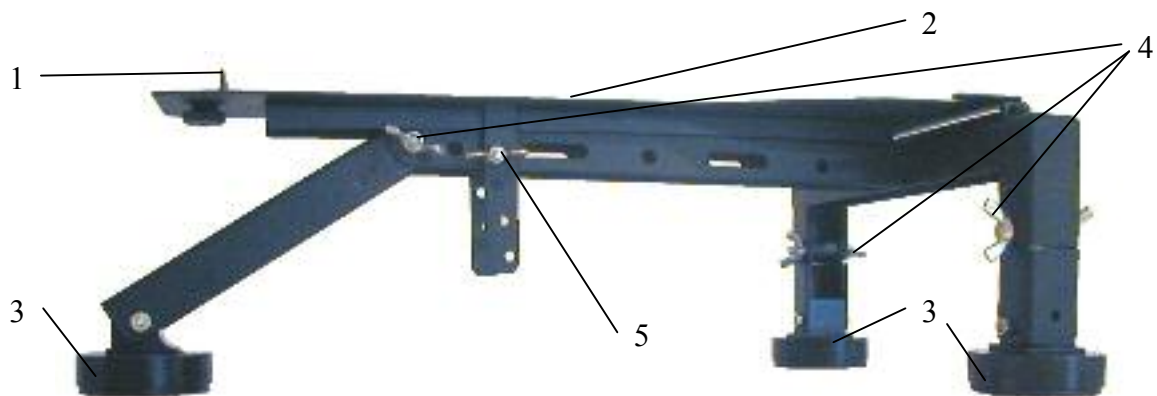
Gestell für die Montage des AMX520/M auf dem Motorrad
